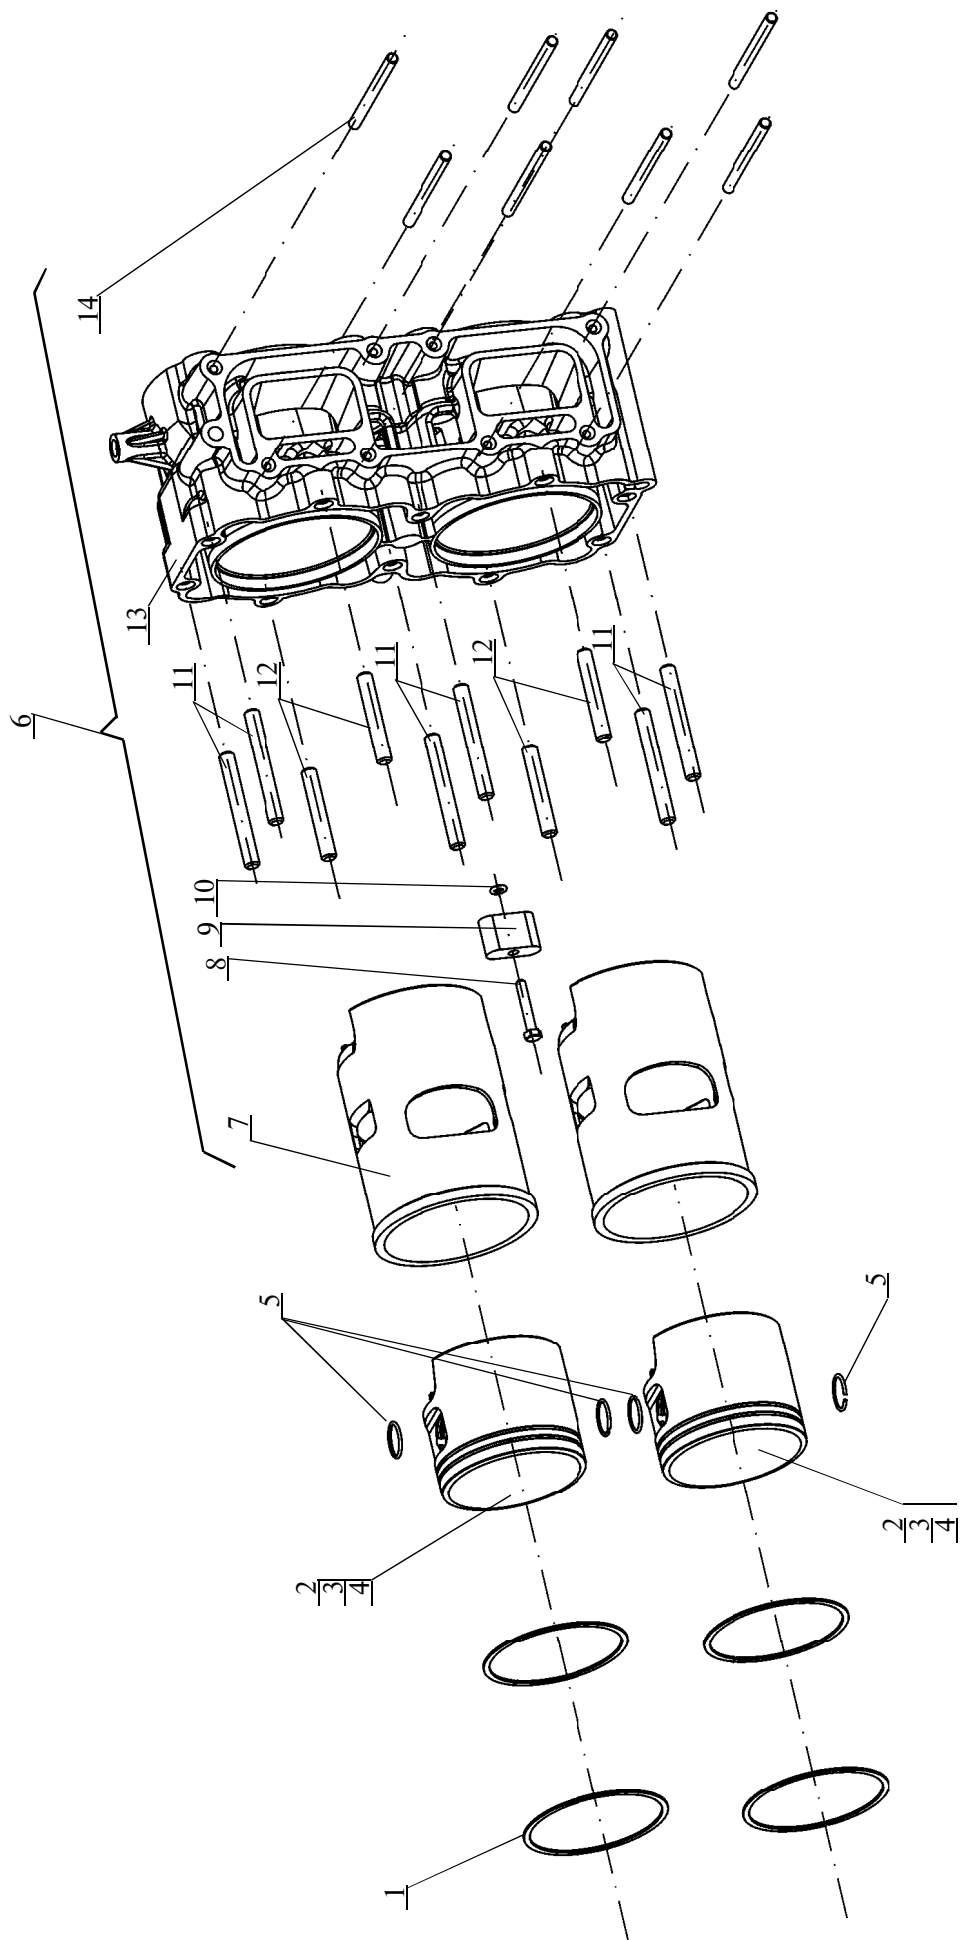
Цилиндро-поршневая группа двигателя
